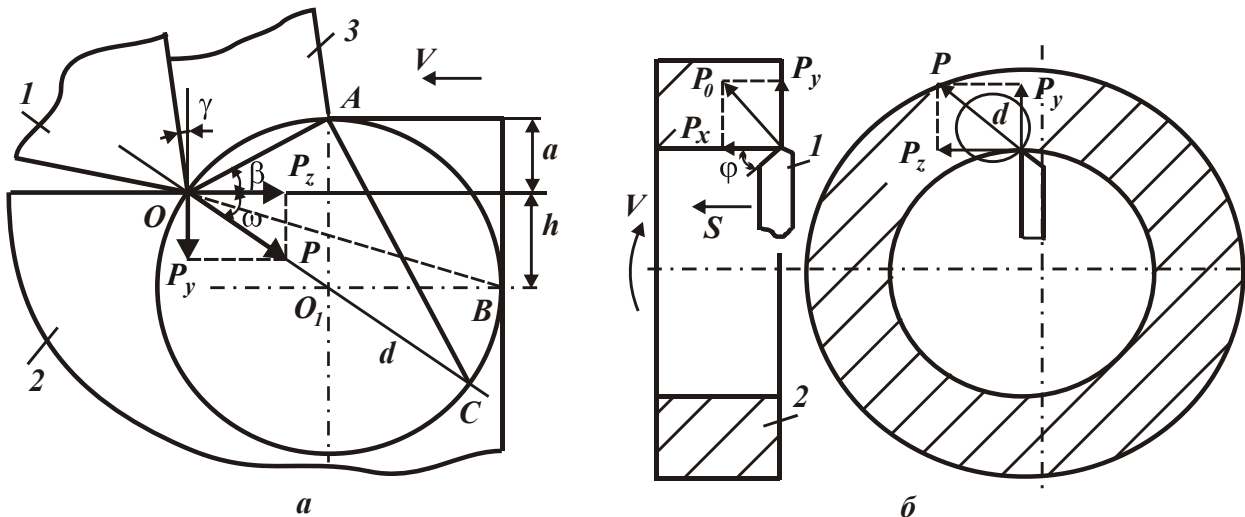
Розрахункові схеми параметрів процесу різання (а) і обробки отвору (б): 1 – різець; 2 – оброблювана деталь; 3 – стружка.
